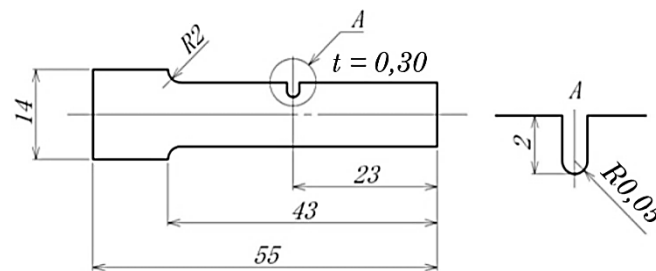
Форма и размеры образца для испытаний на усталость [4]
